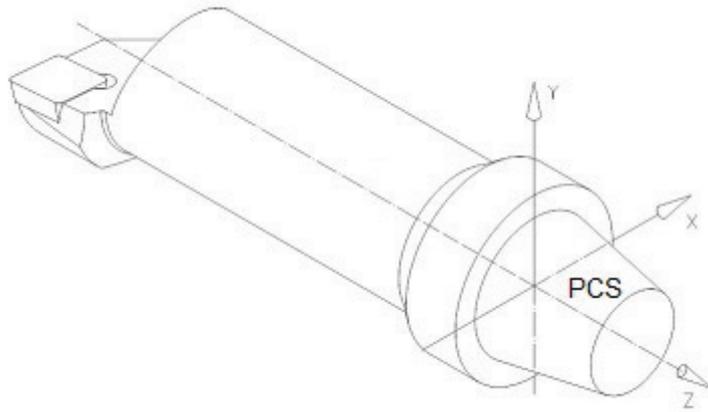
Position de l'outil rond — Plan de jauge ou surface de contact planaire
